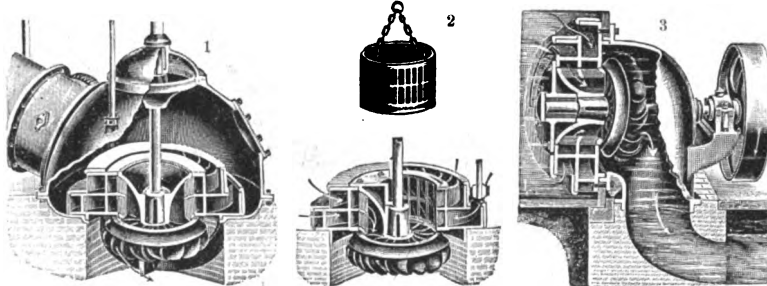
Centripetalturbinen der Maschinenbau-A.-G. Golzern.
